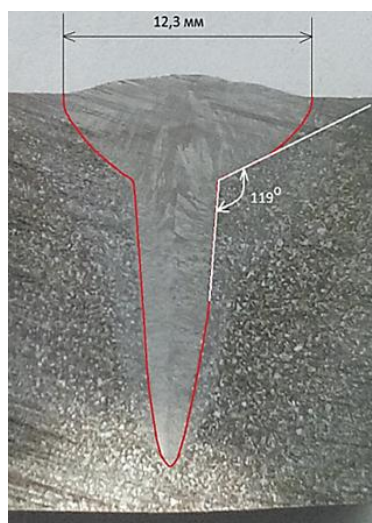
Поперечное сечение шва из сплава ЭП718-ИД при скорости сварки 15 м/ч
